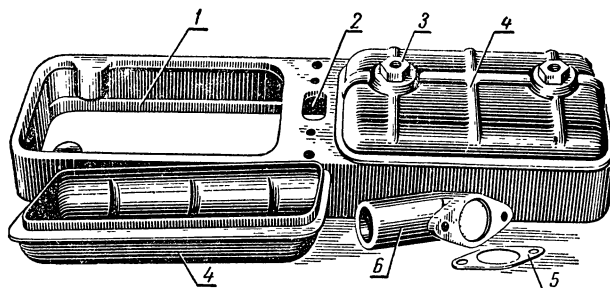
Колпак головки цилиндров дизелей Д-54А и Д-75:
